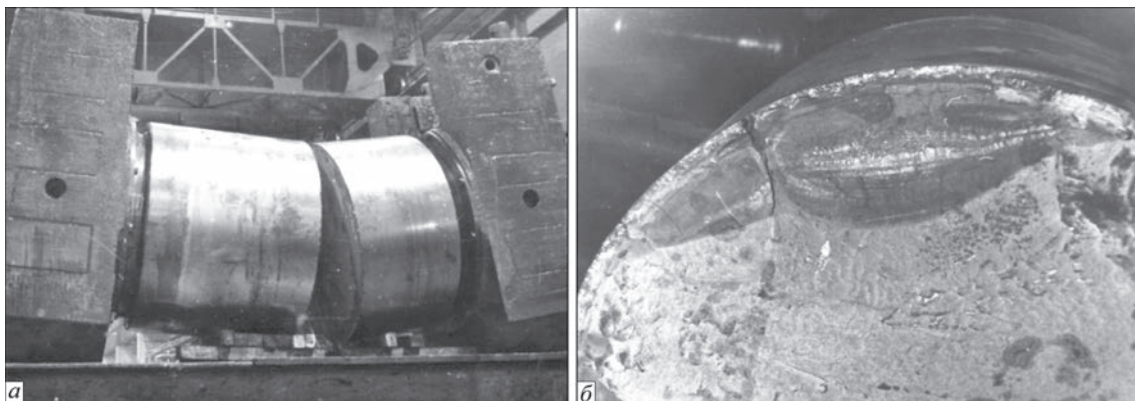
Втомне руйнування наплавленого прокатного валка: а – зовнішній вигляд валка з підшипниковими вузлами після руйнування; б – макробудова зони зародження та поширення тріщини [5]
